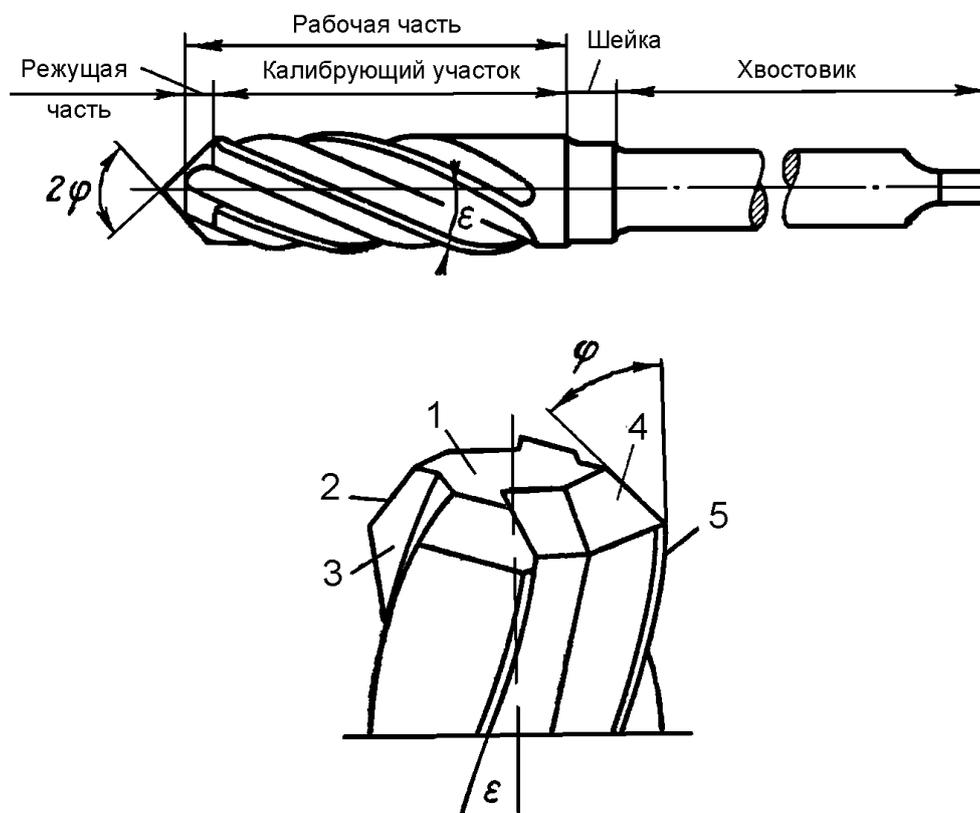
Зенкер, его части и элементы: 1 – сердцевина; 2 – режущая кромка; 3 – передняя поверхность режущей кромки; 4 – задняя поверхность режущей кромки; 5 – ленточка
